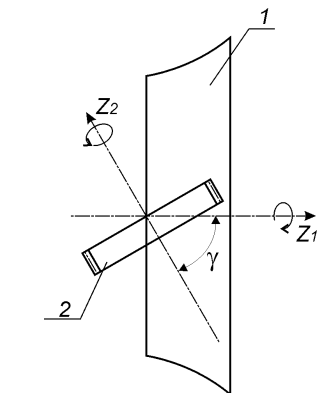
Схема формообразования квазиглобоидной заготовки (колеса)
